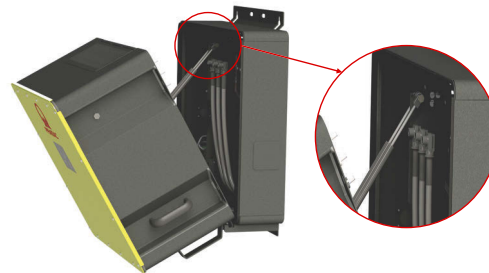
Einhängen der Hydraulikzylinder an der Connection Box
